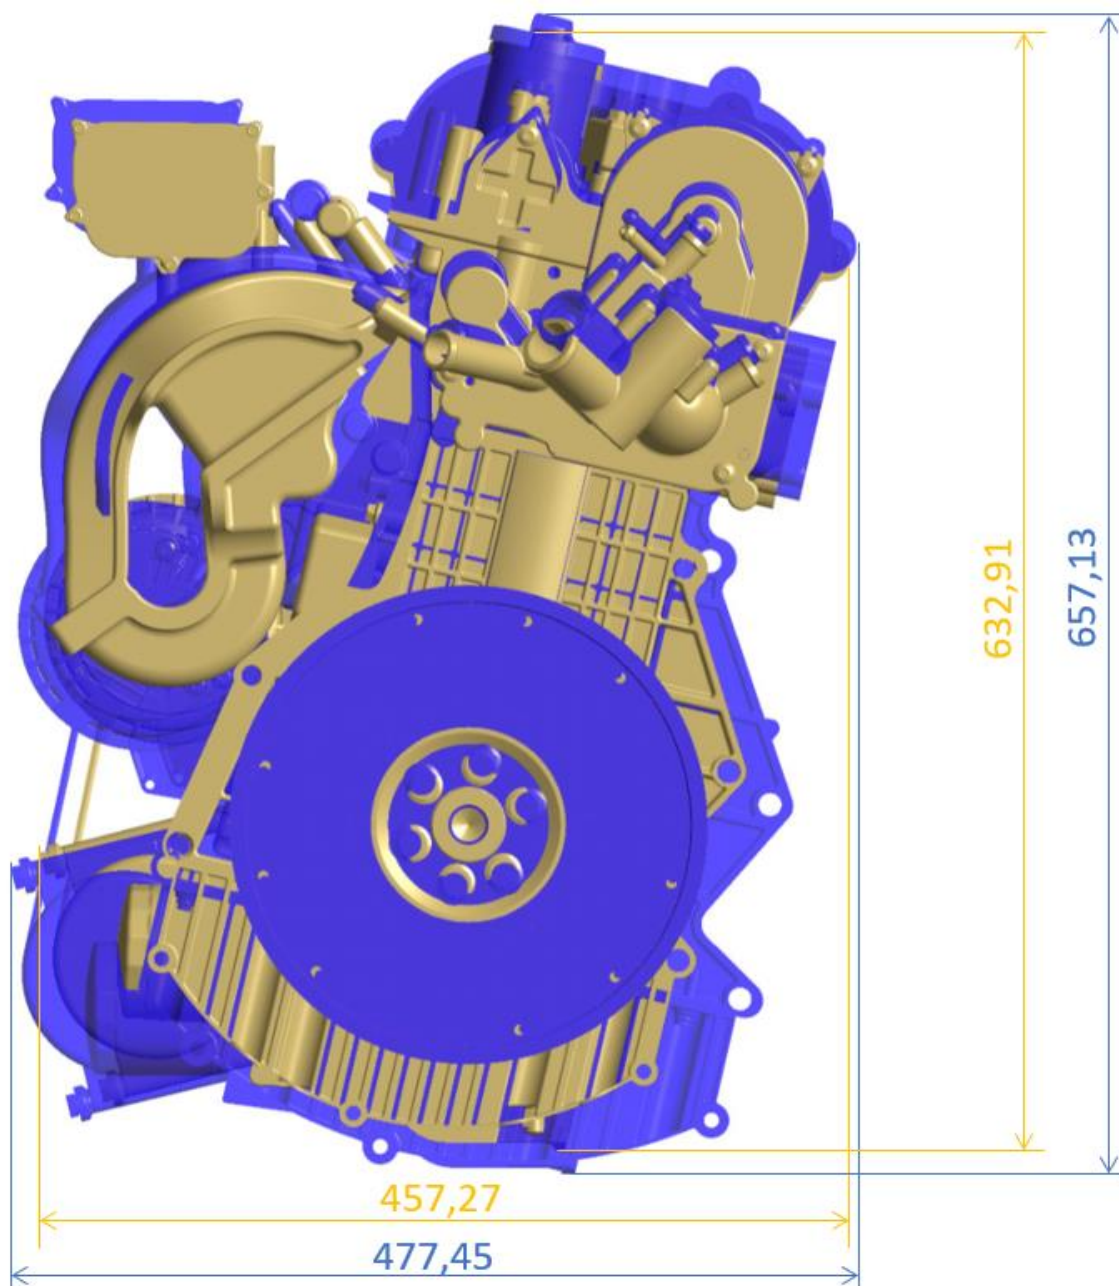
Sestava obou motorů pro porovnání zástavbových rozměrů
